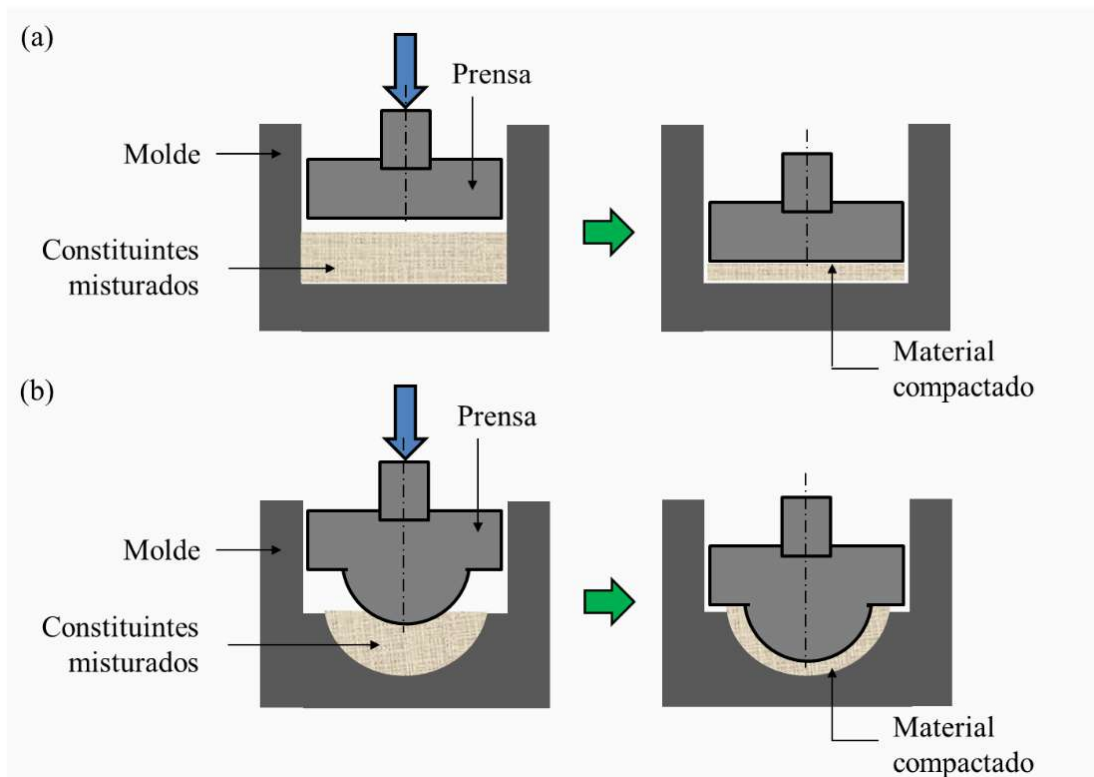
Representação do Processo de Moldagem de Materiais de Atrito Aplicados a Freios:
